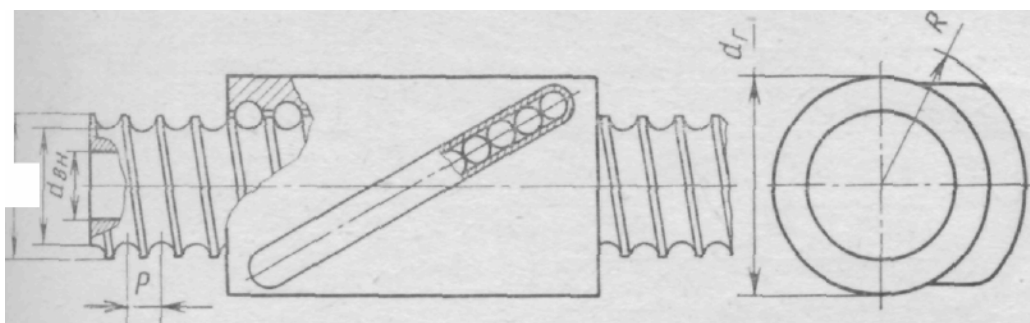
Конструктивная схема винтовой пары качения подающего механизма.
